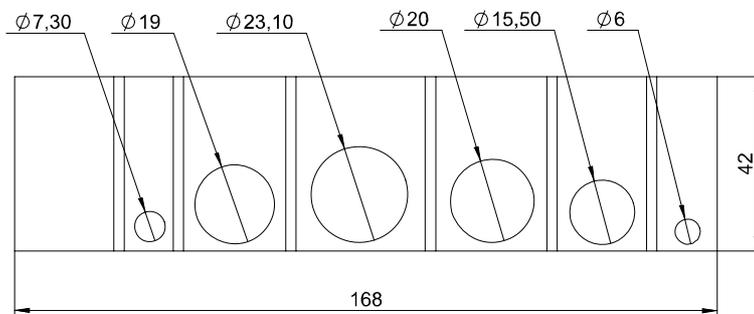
Dimensions pour la chaîne de câbles, IRBT 4003S
